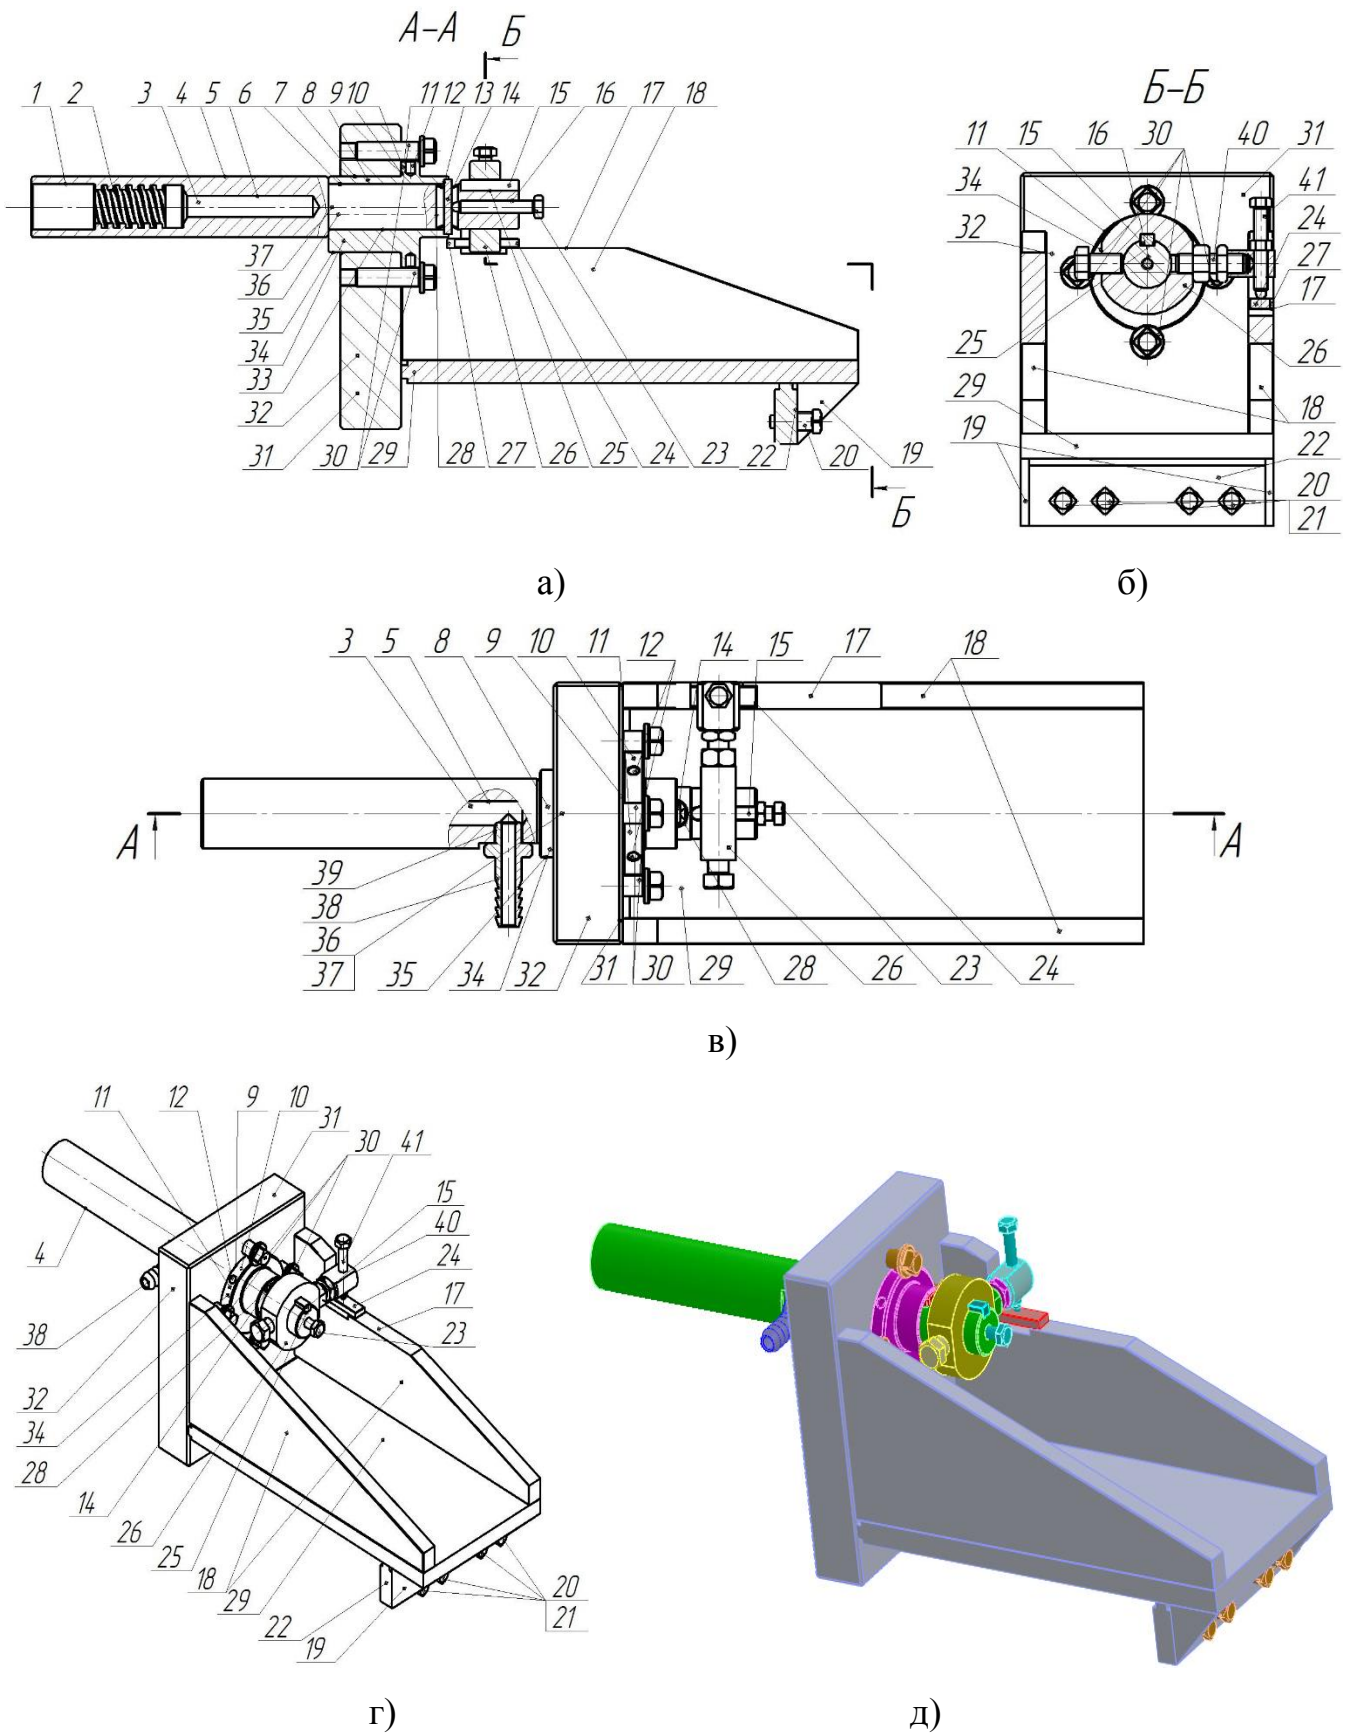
Спеціальний пристрій для оброблення циліндрів з глибокими отворами на токарному верстаті: а) головний вигляд – розріз по А-А; б) вигляд зверху; в) розріз по Б-Б; г) аксонометрія; д) 3-D модель
